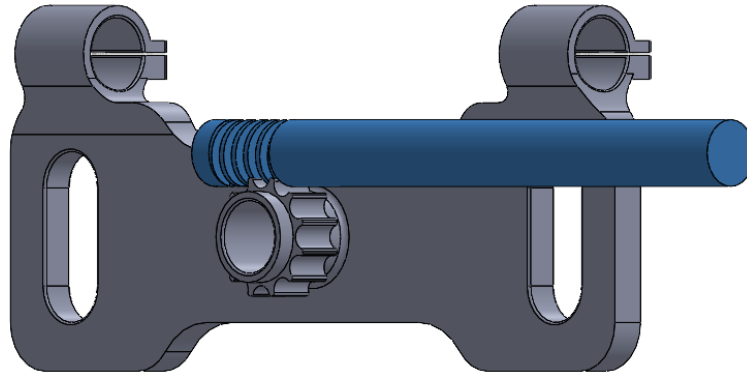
Prototipo 2 de balancín con engranaje y conectado a un eje con tornillo sin fin.
